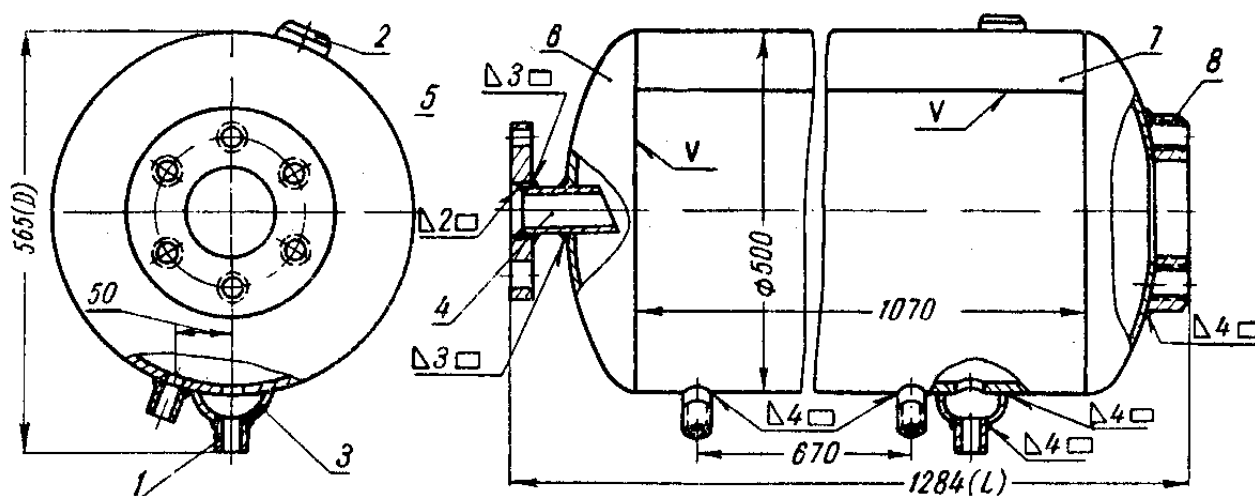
Загальний вигляд повітряного ресивера
